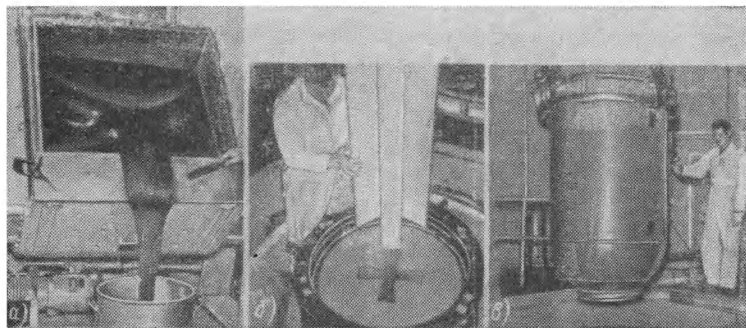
Двигатель с монолитным заливаемым в корпус зарядом твердого топлива (США):
